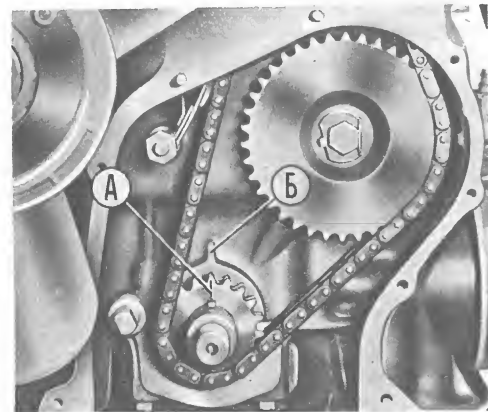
Установка ведущей звездочки цепного привода: А и Б — контрольные метки.
